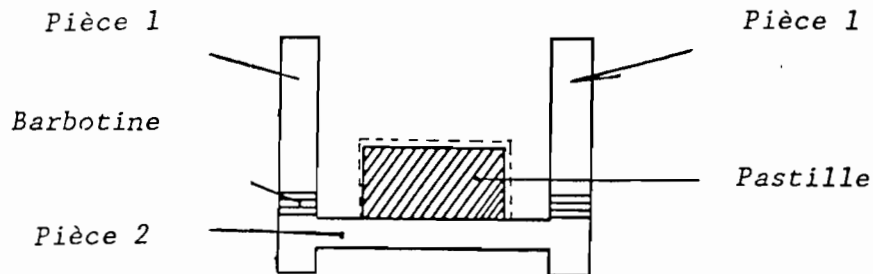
Creuset obtenu par superposition de pièces de carbure de silicium densifié à chaud.
